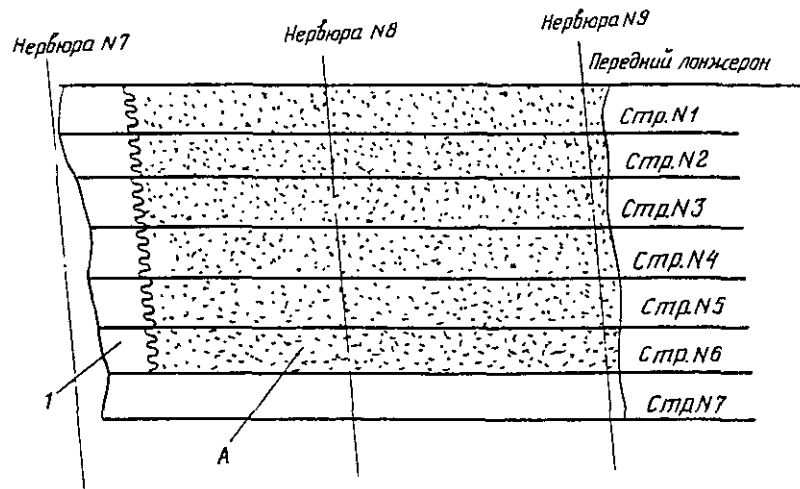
Нижняя панель СЧК между нервюрами № 7—9 от переднего лонжерона до стр № 6
